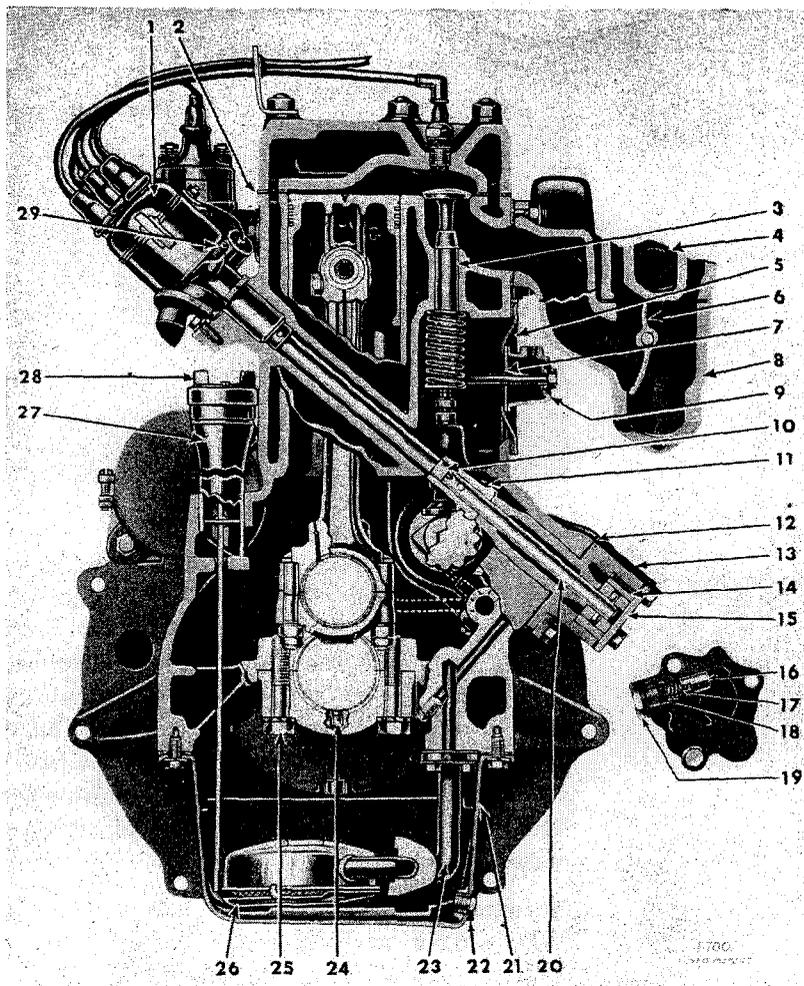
Vierzylinder L-Kopf - Motor. Seitenschnitt
